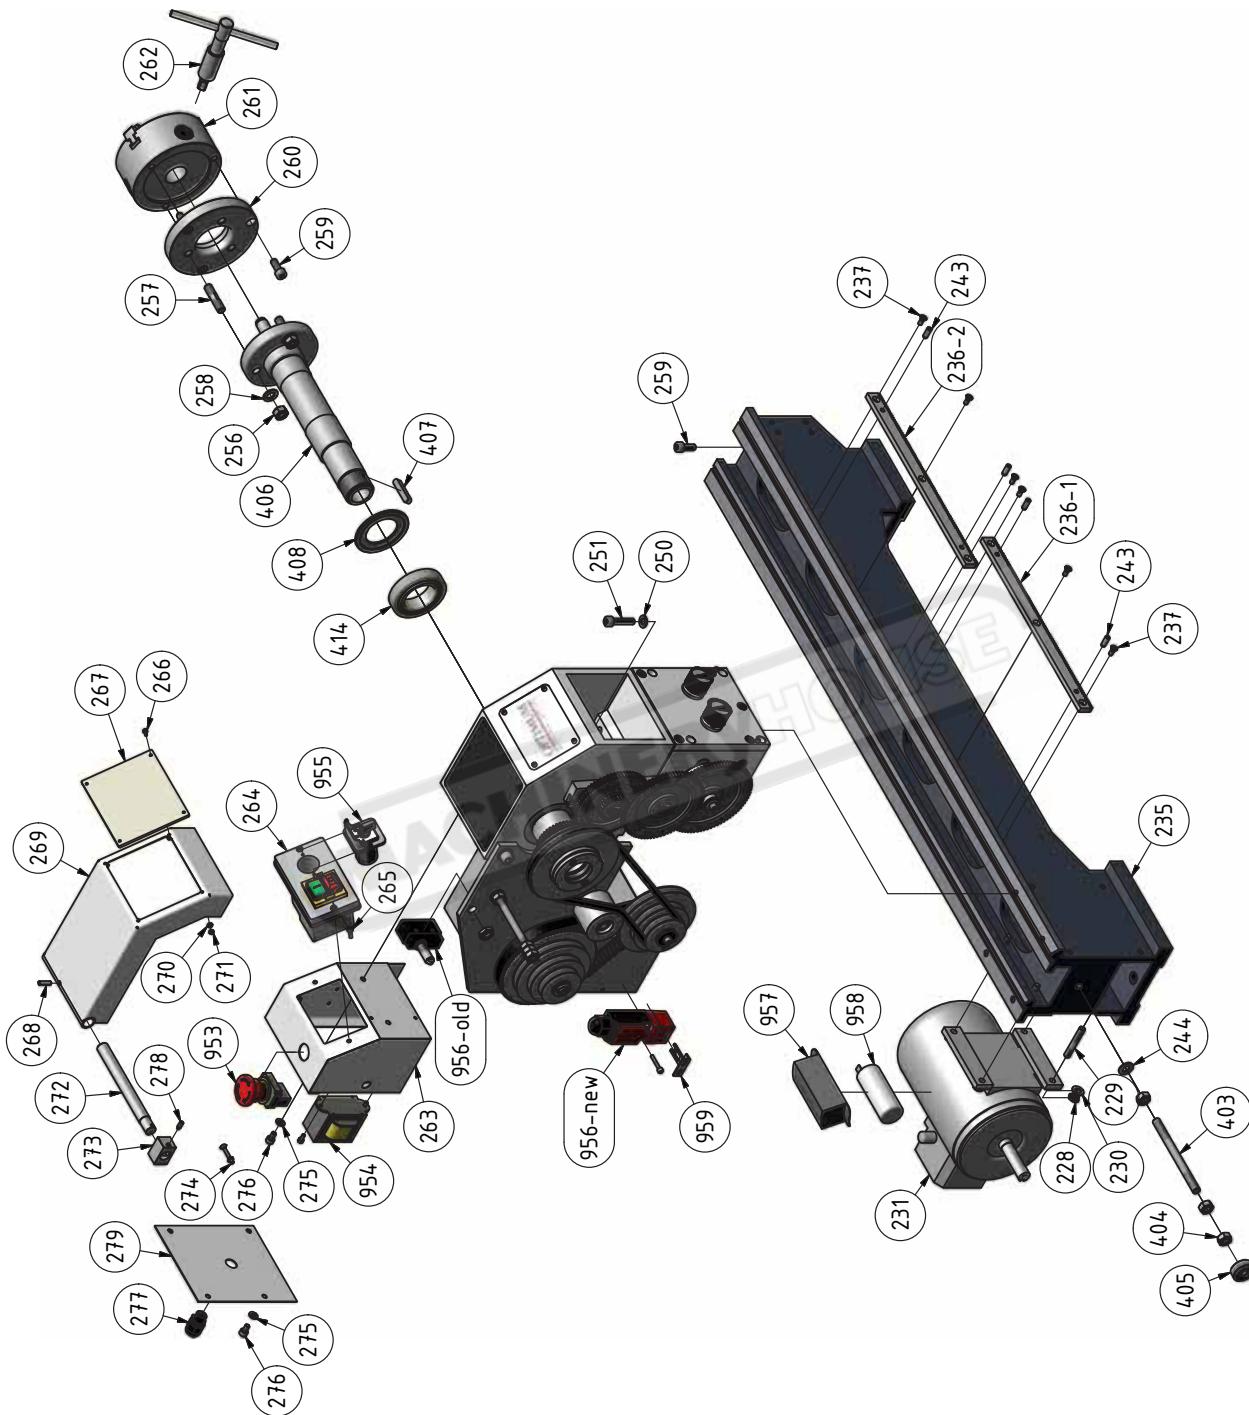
Spindelstock - Headstock 2 of 2 - TU2506
